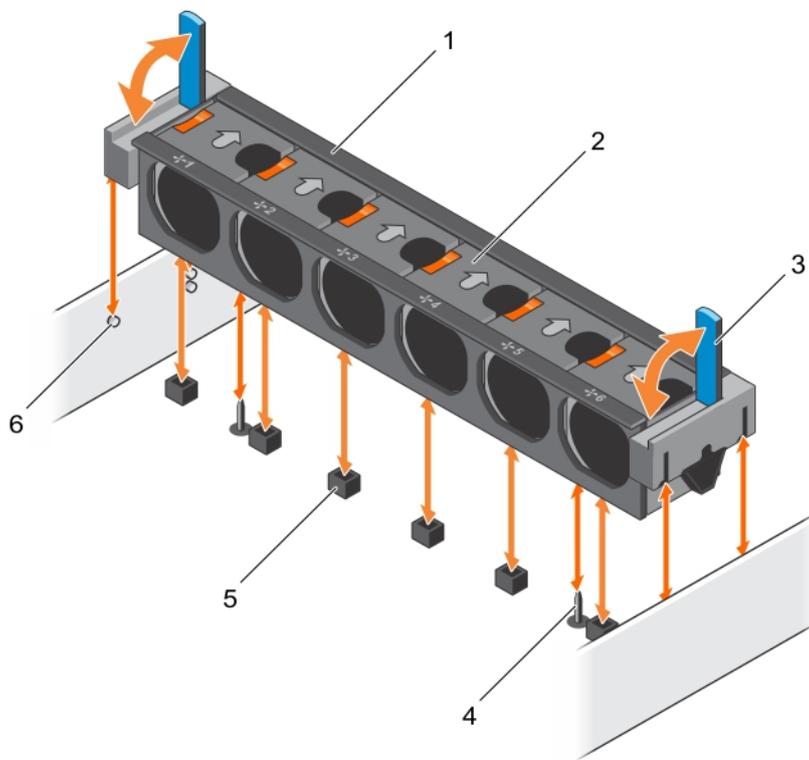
Entfernen und Installieren der Lüfterbaugruppe
